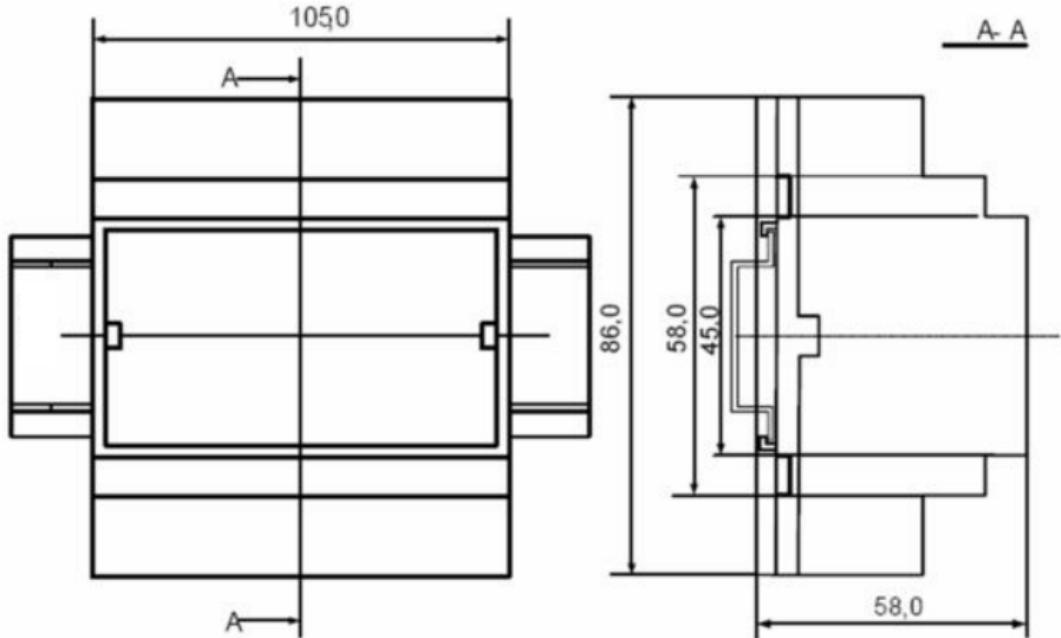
Габаритные и присоединительные размеры блока питания и реле
